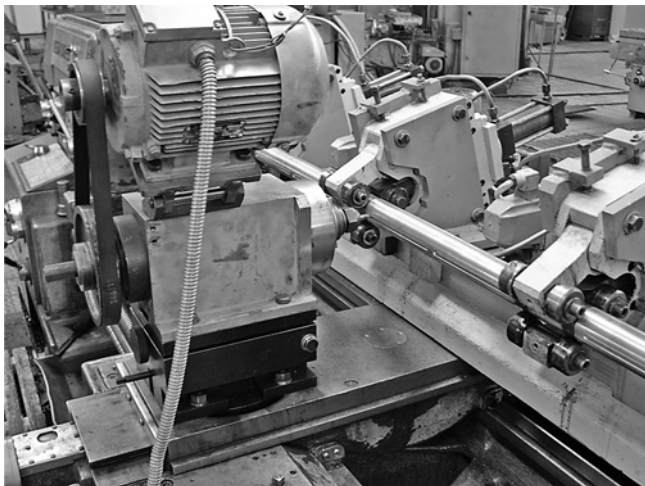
Общий вид установки с зоной СЦЛ фрезерования
